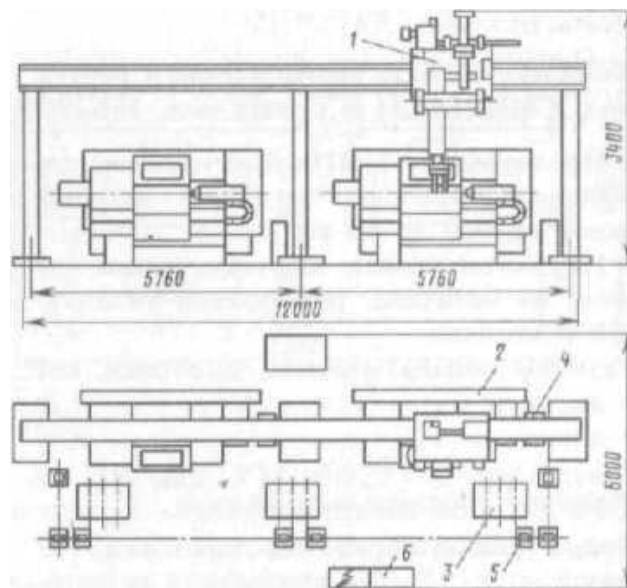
Комплекс мод. Асвр-041: 1 - ПР мод. СМ40Ф2.80.01 портального типа; 2 — токарный станок мод. 16К20Т1 с ЧПУ*1; 3 — магазин; 4 — промежуточная позиция; 5 — система светозащиты; 6 — устройства управления ПР
